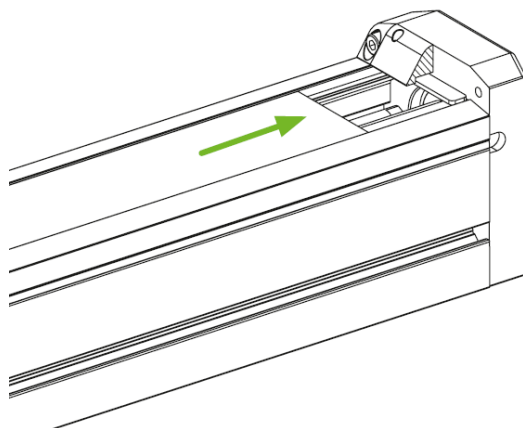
Démontage/montage du dispositif de serrage de la bande de recouvrement des modules linéaires pour HM-S
